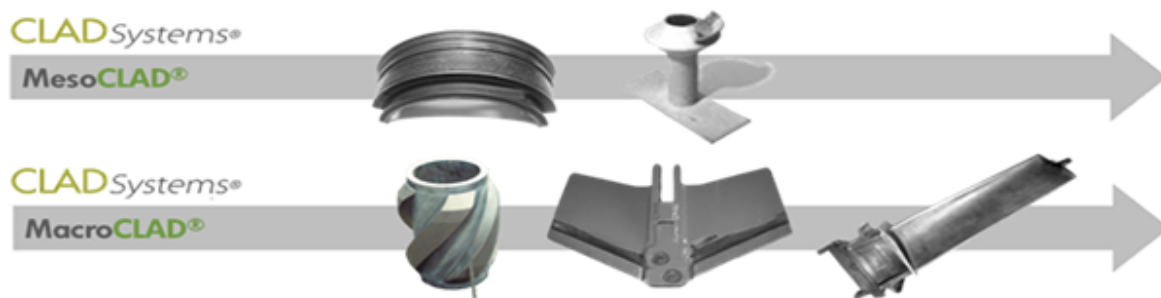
Géométries réparables en fabrication additive laser par projection de poudre (procédé CLAD de BeAM)
